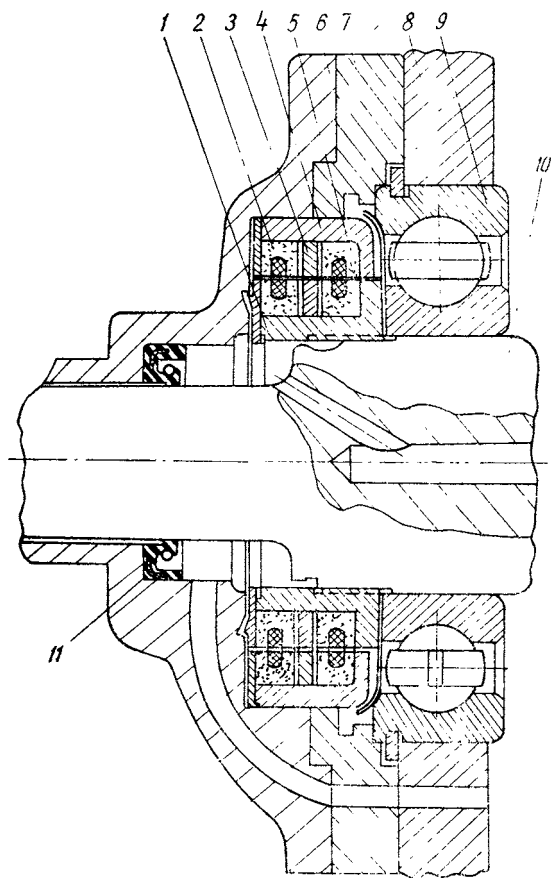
Проходное бесконтактное токосъемное устройство для первичного вала коробки передач: 1 — обойма внутренних колец; 2 — питающий трансформатор; 3 — экран; 4 — обойма наружных колец; 5 — измерительный трансформатор; 6 — фланец; 7 — проставка; 8 — картер коробки передач; 9 — подшипник первичного вала; 10 — первичный вал; 11 — сальник
